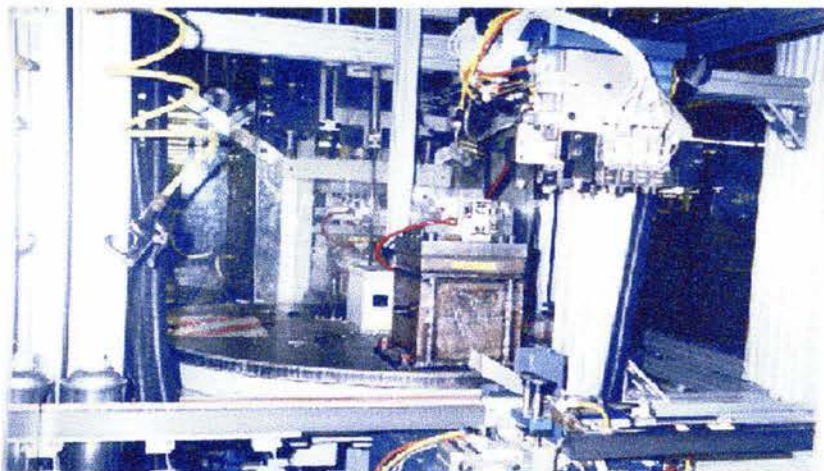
Máquina moldeadora. (Cortesía de Midcom Inc.)
